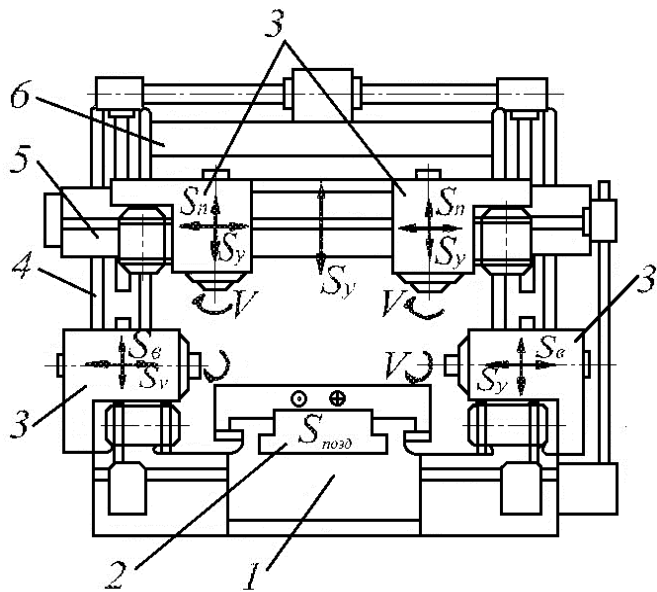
Загальний вигляд поздовжньо-фрезерного верстата з двома стояками
